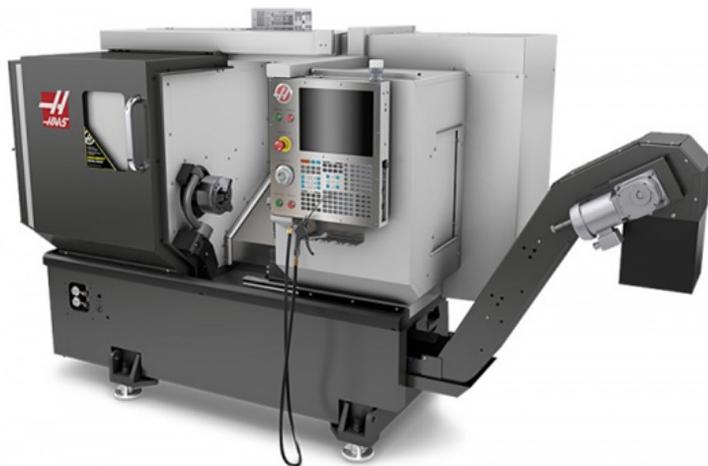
Токарно-револьверный станок Haas ST-10Y с ЧПУ
